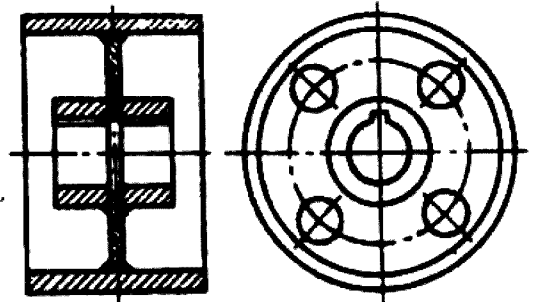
Ротор синхронной машины в виде сварного магнитного колеса
